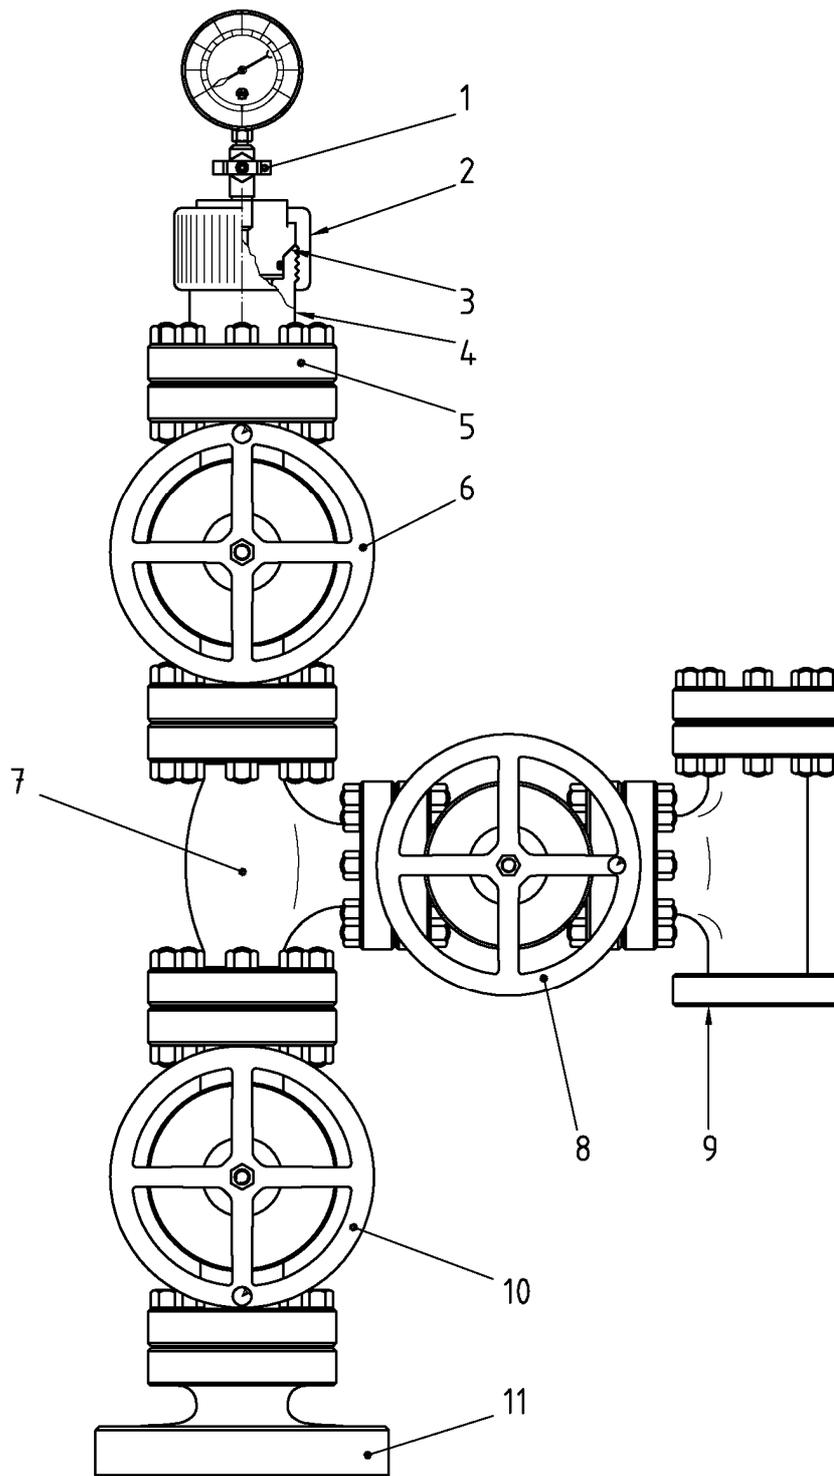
Наименование деталей и сборочных единиц типового устьевого оборудования в сборе
